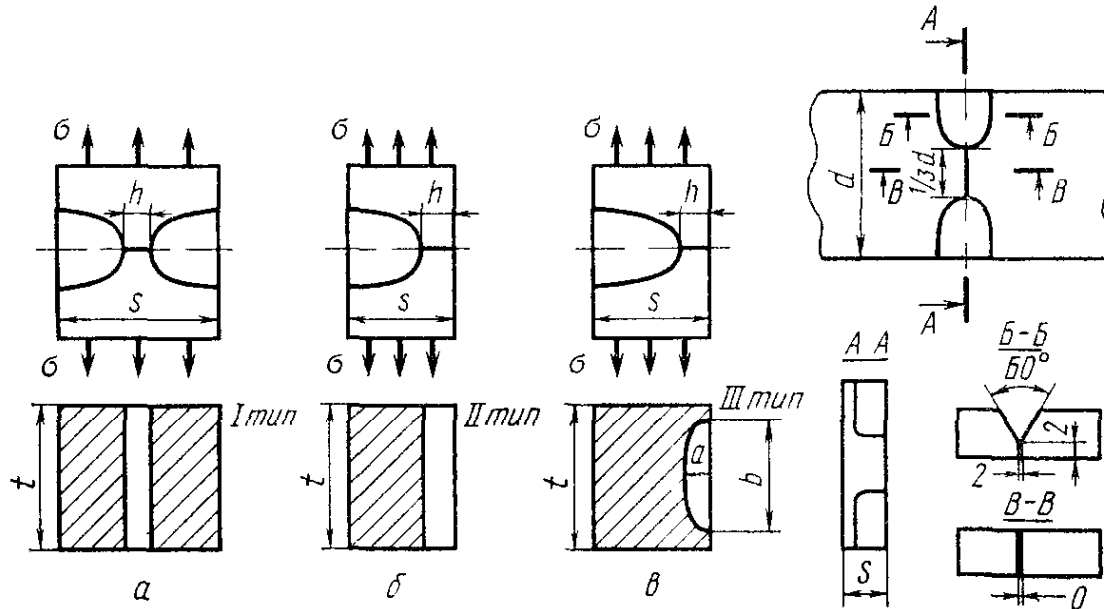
Сварные образцы для испытаний на трещиностойкость
